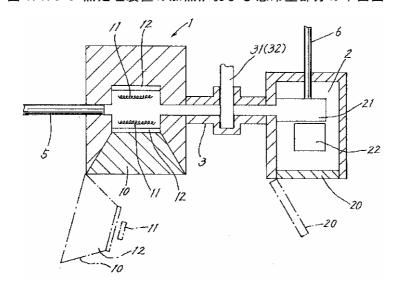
熱処理装置の加熱炉および急冷室部分の平面図
